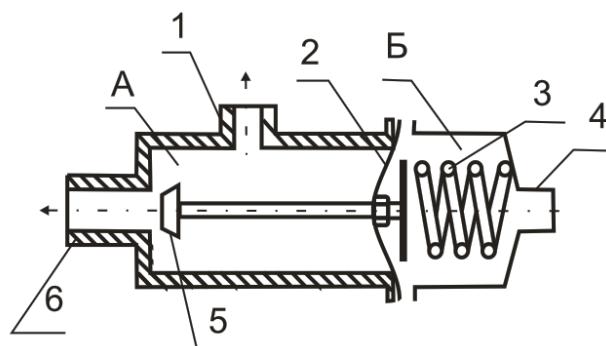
Регулятор давления топлива: 1 – входной патрубок топлива; 2 – диафрагма; 3 – пружина; 4 – вакуумный патрубок; 5 – клапаны; 6 – патрубок отвода топлива в бак.
